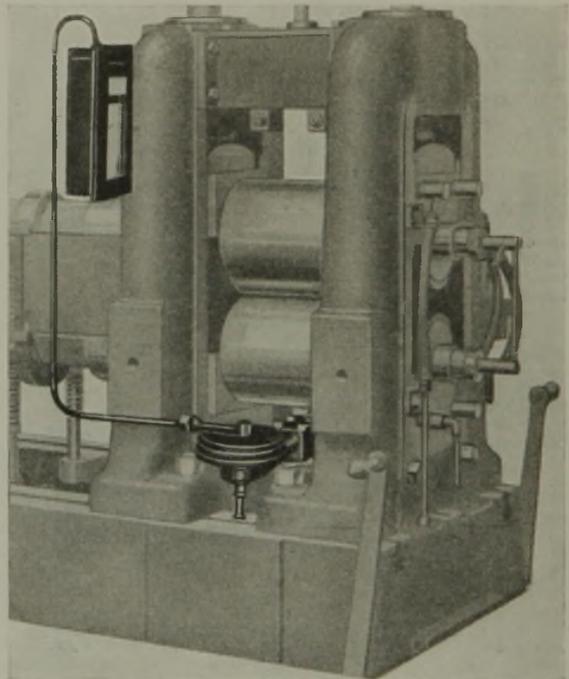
Walzendruck-Prüfgerät Pasopos am Walzgerüst.
